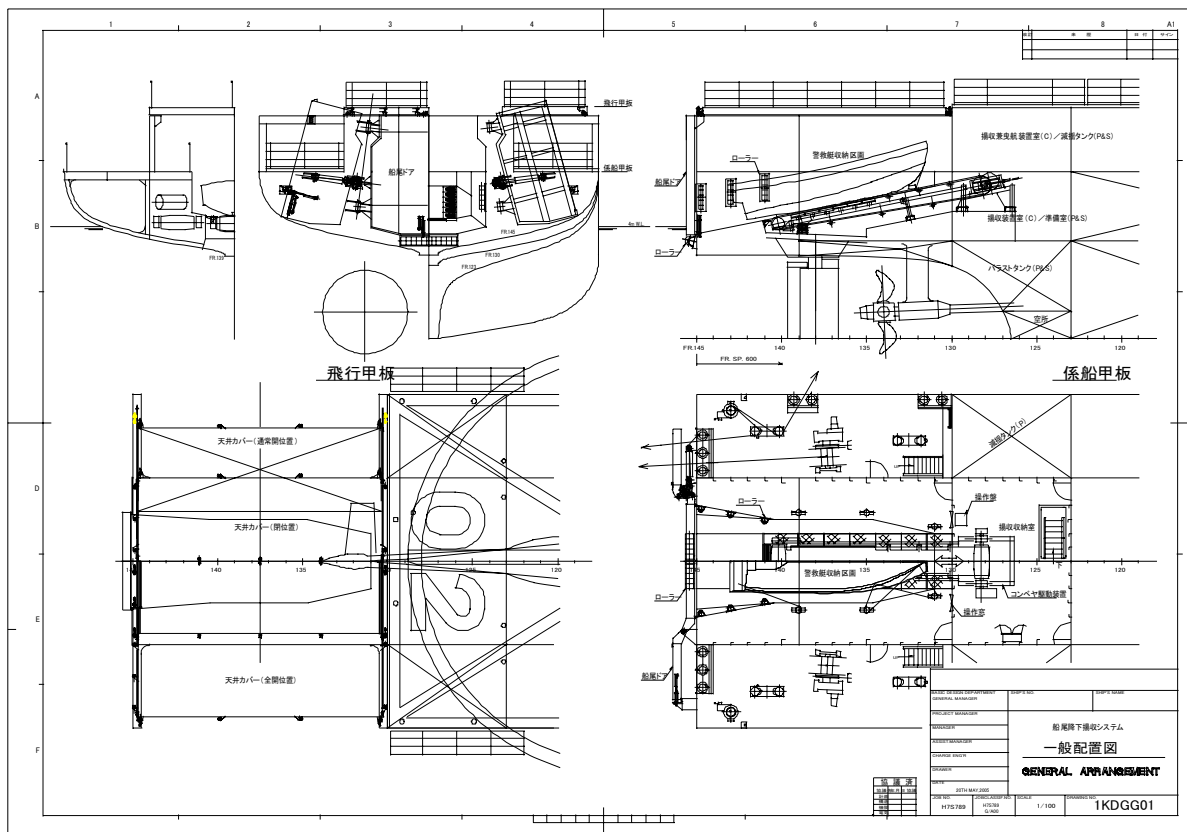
ベルトコンベア方式 船尾一般配置図
